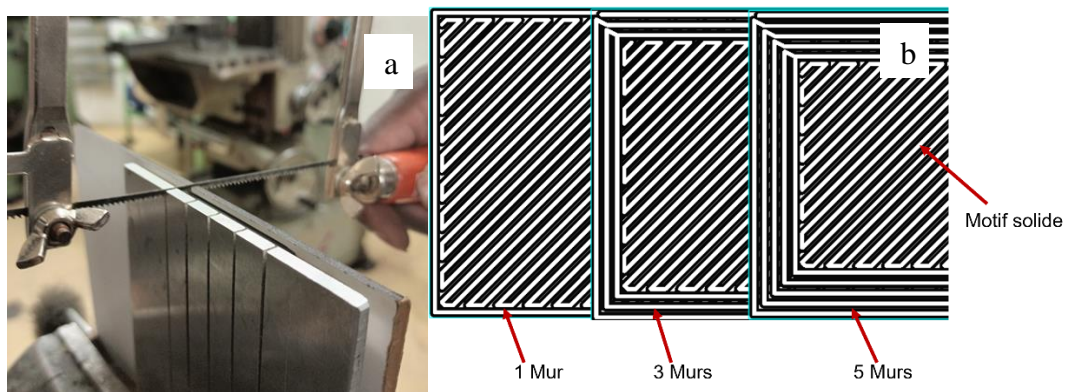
a) Technique de découpe des éprouvettes Onyx et b) disposition des murs.
